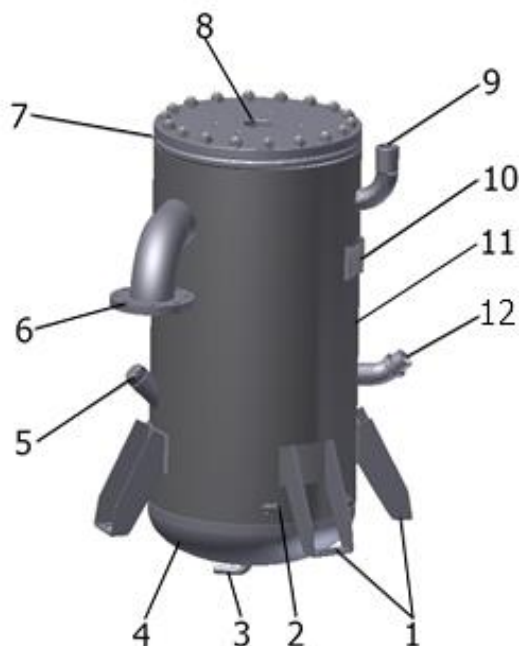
Сепаратор: 1 – опоры; 2 – днище; 3 – трубка для слива масла; 4 – днище; 5 – горловина маслоналивная; 6 – труба подвода масलोвоздушной смеси; 7 – крышка; 8 – место установки клапана минимального давления; 9 – трубка крепления предохранительного клапана; 10 – табличка с маркировкой; 11 – корпус сепаратора; 12 – труба для отвода масла
